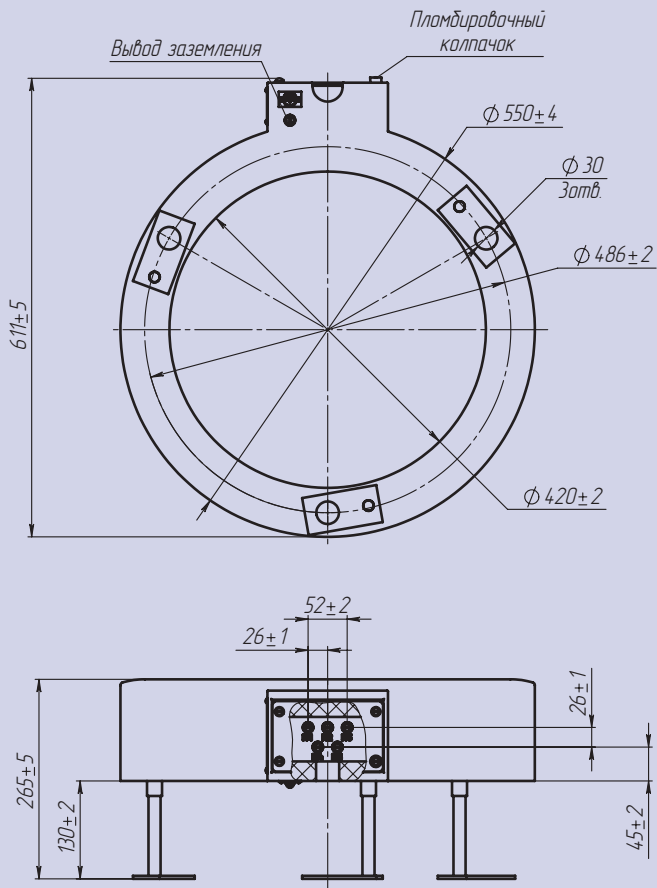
Габаритные, установочные и присоединительные размеры трансформатора ТВ-110-IX
